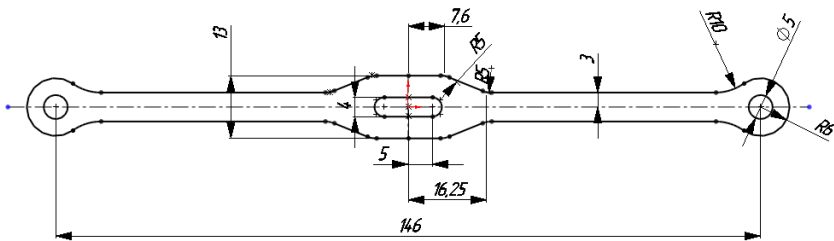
Ескіз розгорнення деталі Скоба
